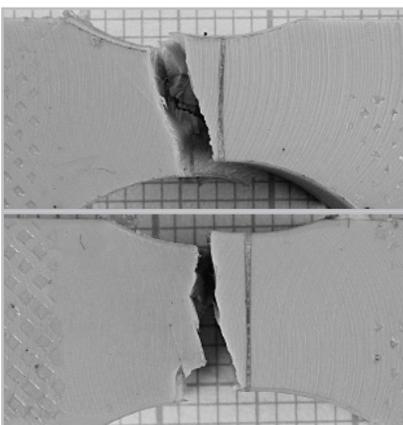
Сварные соединения образцов из PEEK, сваренные на «мягких» режимах после механических испытаний
